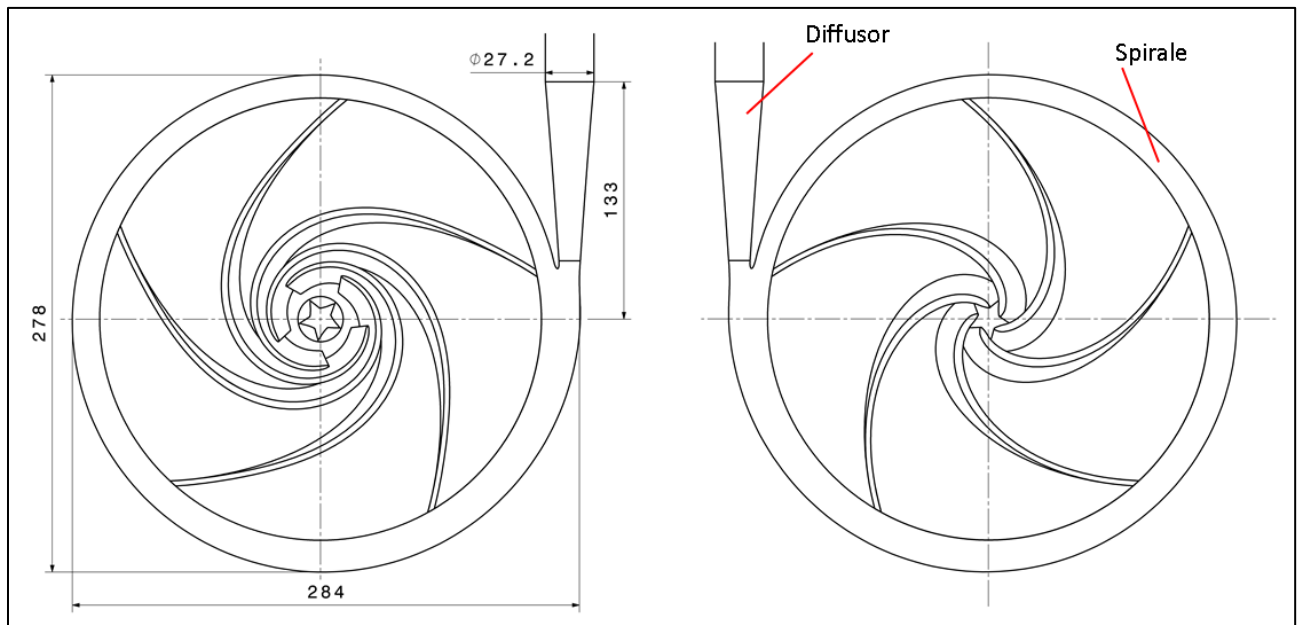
Draufsicht (links) und Rückansicht (rechts) der Pumpe für die gusstechnische Fertigung mit  $n_q = 6 \text{ min}^{-1}$
